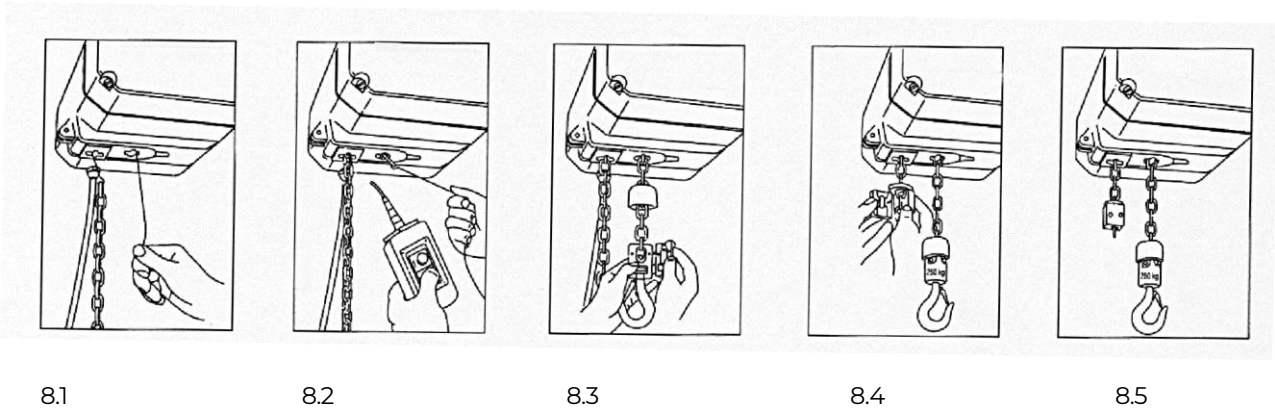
Auflegen der Lastkette bei einsträngiger Ausführung (außer Bauform B6.1, B8.1)
